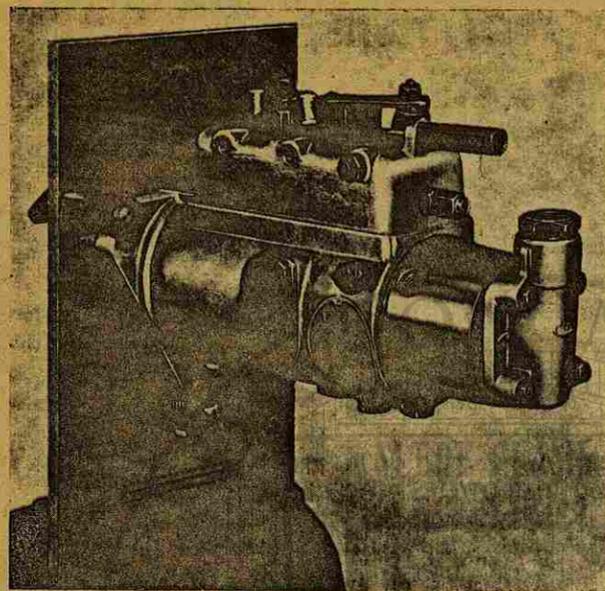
Bomba con regulador mecánico montada sobre dispositivo para su montaje y desmontaje
